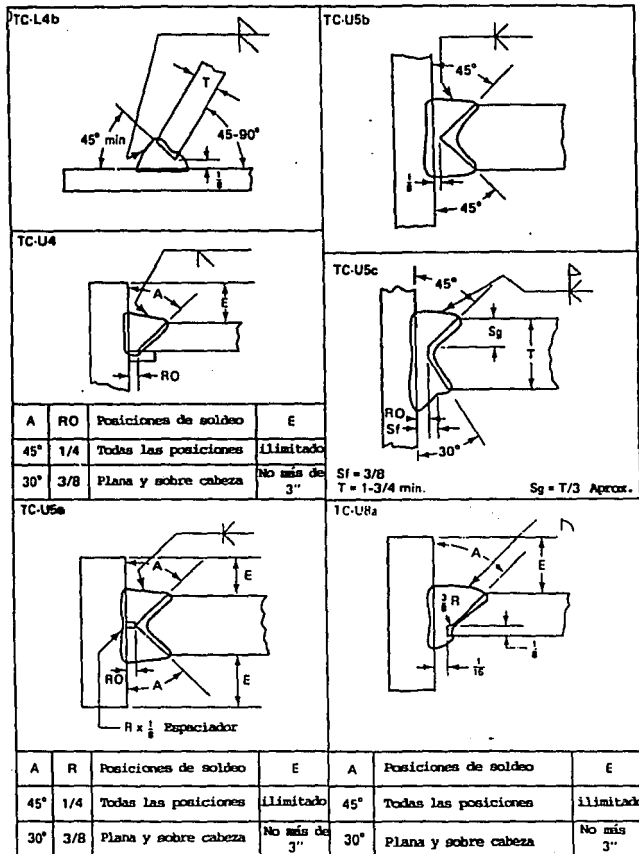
Diseño de uniones soldadas (cont.).
